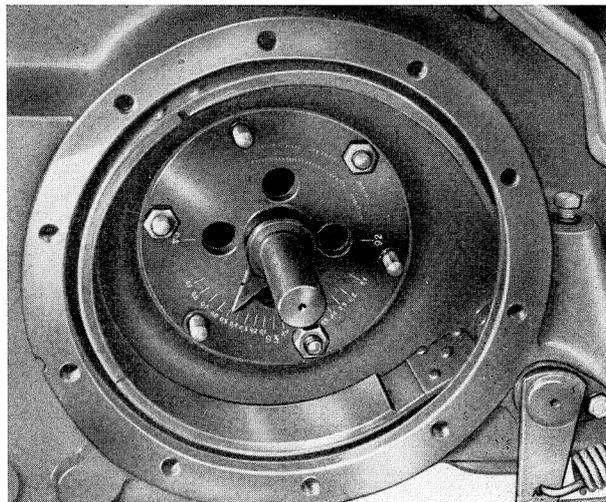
Vue latérale (droite) de l'outil A 137010 pour le réglage du couple conique.
